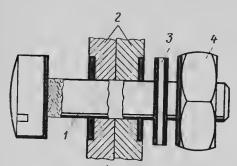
Болтовое соединение (стык) деталей конструкции объекта:
